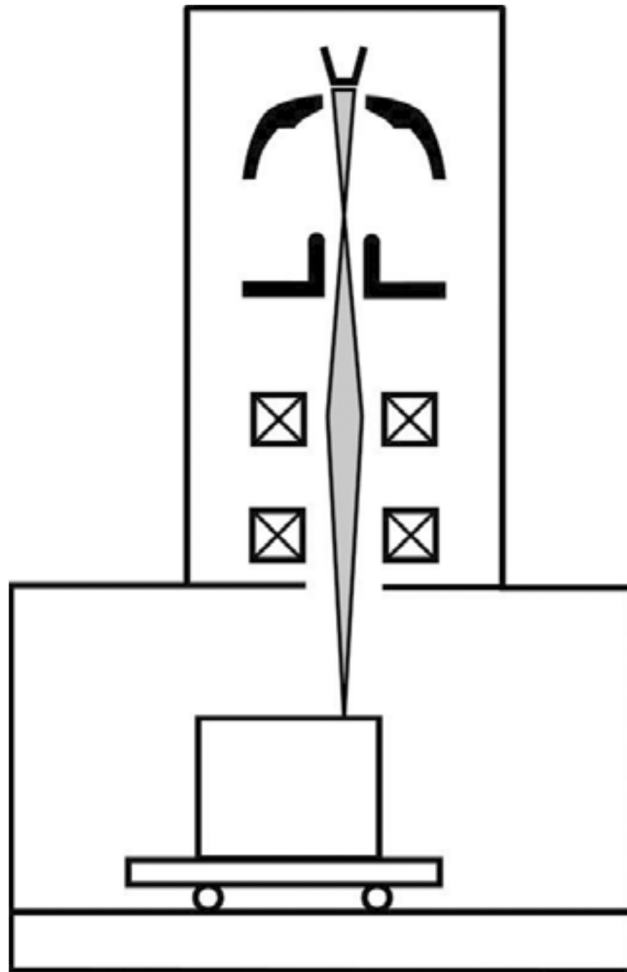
Principe du soudage par faisceau d'électrons. [16]
